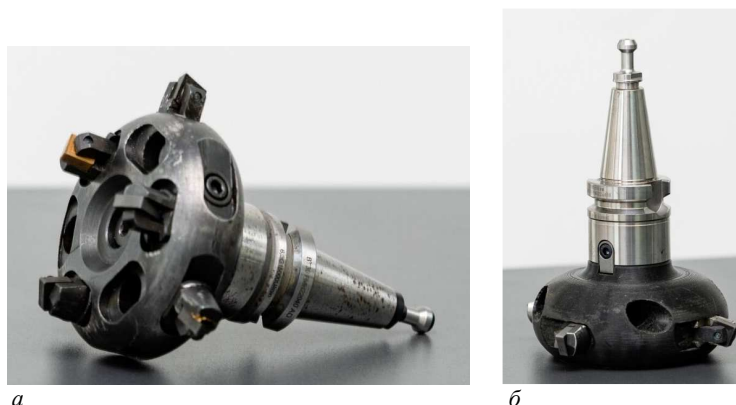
Внешний вид универсальной фрезы из металлических (а) и «гибридных» (б) материалов
